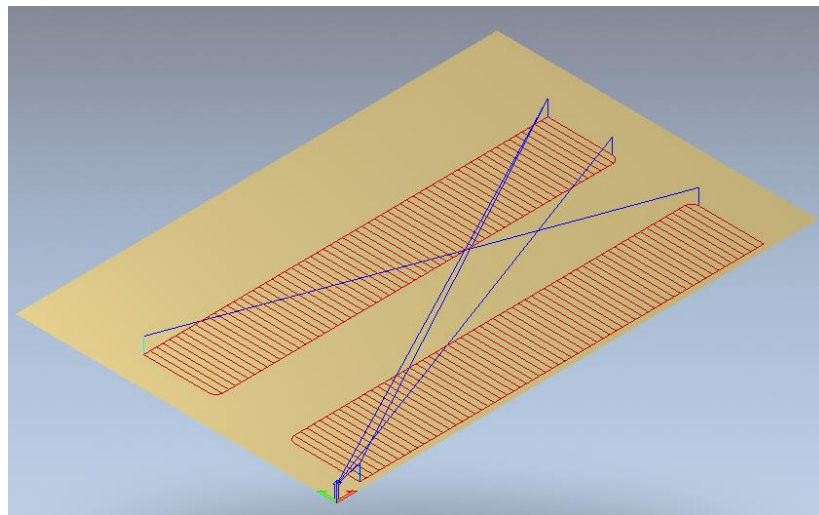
Траектория ruchu інструмента при обробці деталі №6
